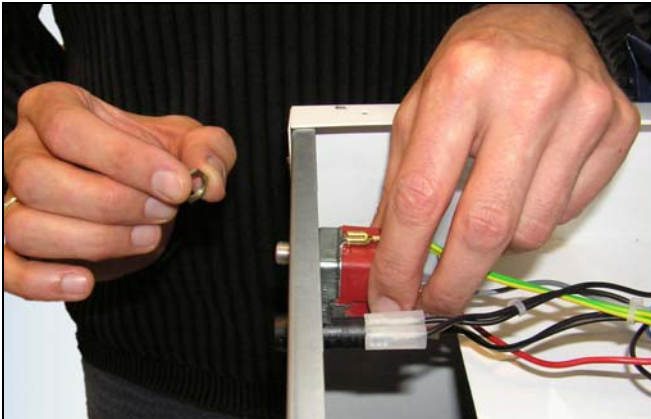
Die Befestigungsmutter des STB abschrauben, diesen von innen durch das Frontverkleidungsblech hindurch stecken und ihn dort von außen mit der Mutter festschrauben.
